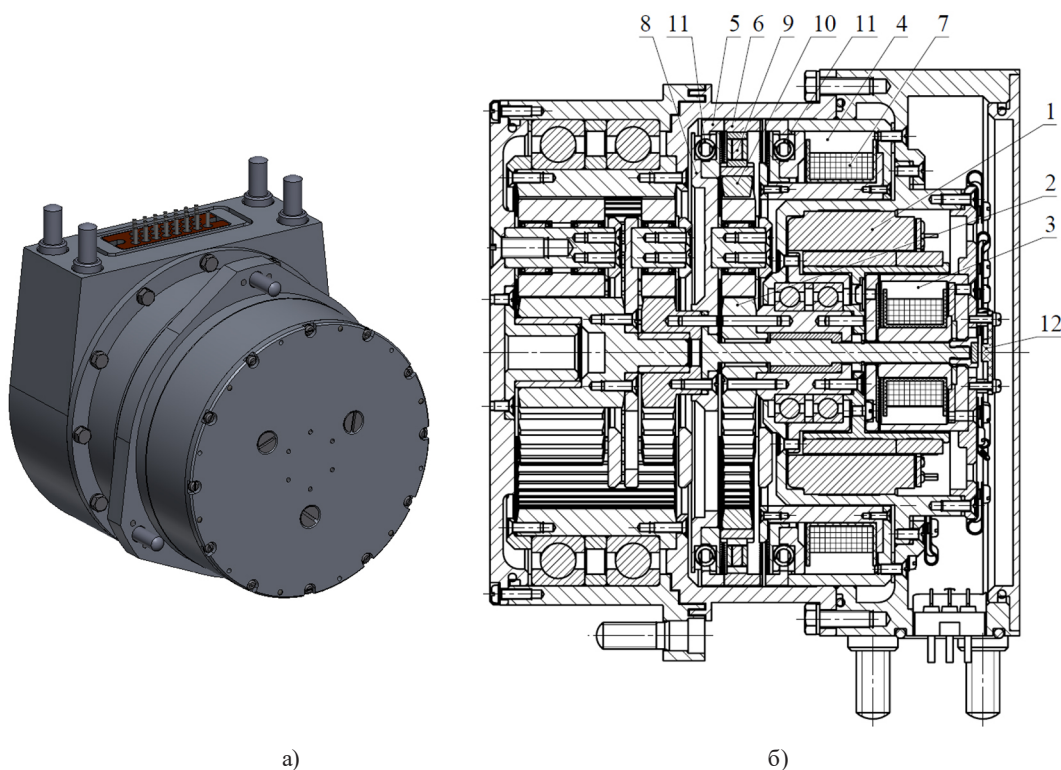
Внешний вид (а) и конструкция (б) приводного модуля: 1 – агрегат приводной; 2 – солнечная шестерня; 3 – электромагнитный тормоз; 4 – статор МИПЧ; 5 – шунт; 6 – якорь МИПЧ; 7 – электромагнитная катушка; 8 – водило; 9 – кольцевой постоянный магнит; 10 – коронная шестерня; 11 – пружинный демпфер; 12 – датчик Холла
